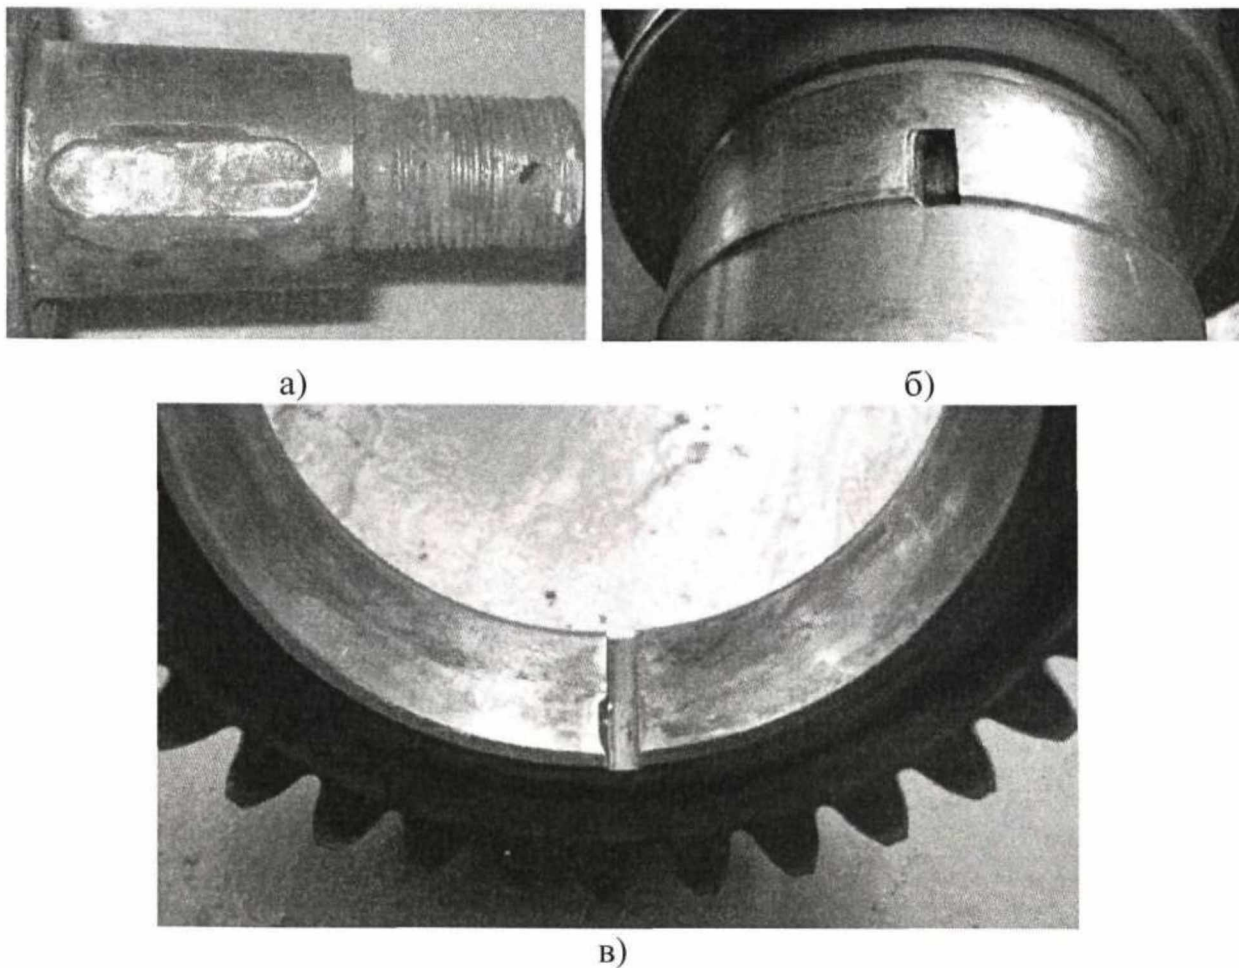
Порушення геометричних форм пазів валу або втулки: а) вал МКШ комбайну «ДОН-1500»; б) колінчастий вал трактора John Deere 9420; в) шестерня газорозподільного механізму трактора John Deere
